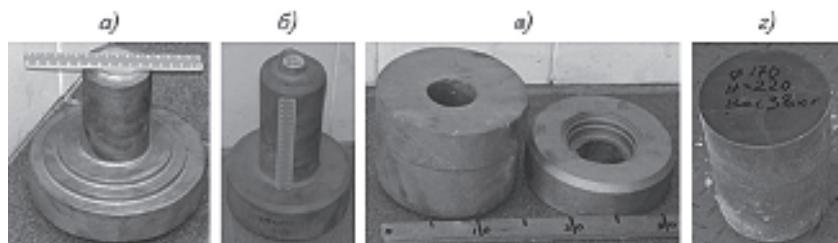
Литые заготовки диска переменного сечения (а), диска с валом (б), кольцевые заготовки (в), цилиндрическая заготовка (г) из сплава ЭП975
